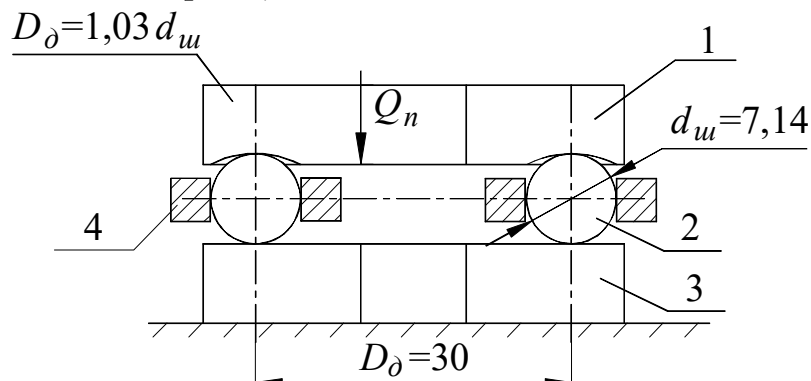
Схема випробувань КП: 1 – верхнє кільце упорного КП; 2 – кульки КП; 3 – випробовуваний плоский кільцевий зразок; 4 –
